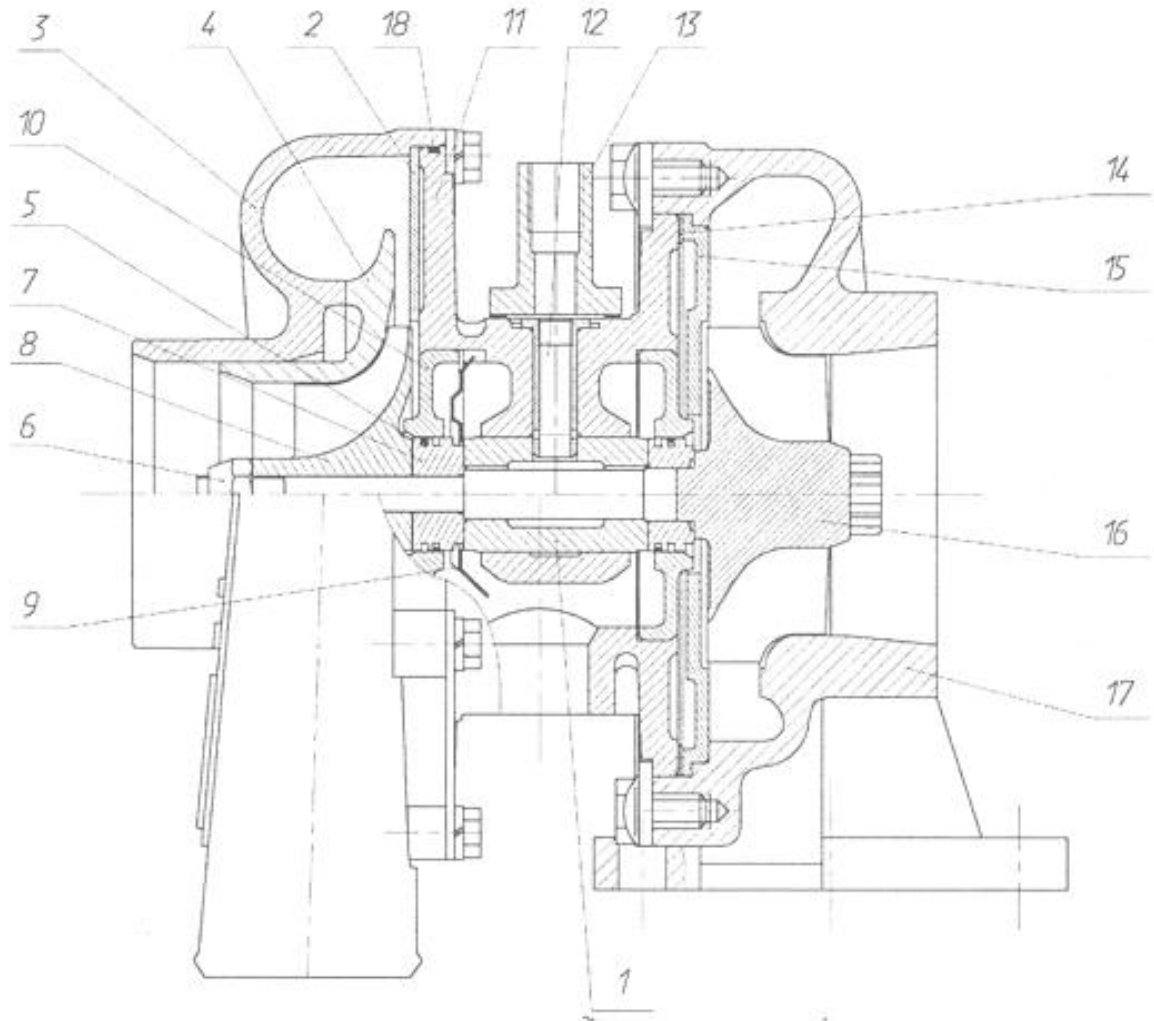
Турбокомпрессор ТКР 7Н-1
